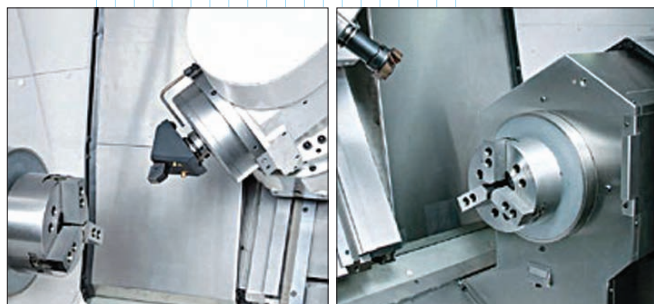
Шпиндели токарно-обрабатывающего центра OKUMA MULTUS B300
